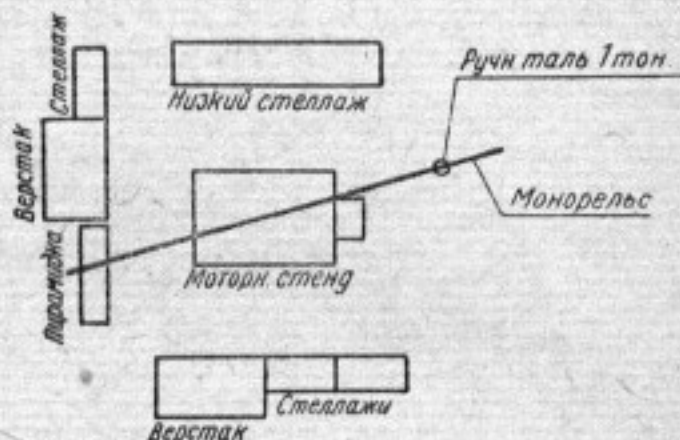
Планировка рабочего места бригады по ремонту двигателей
